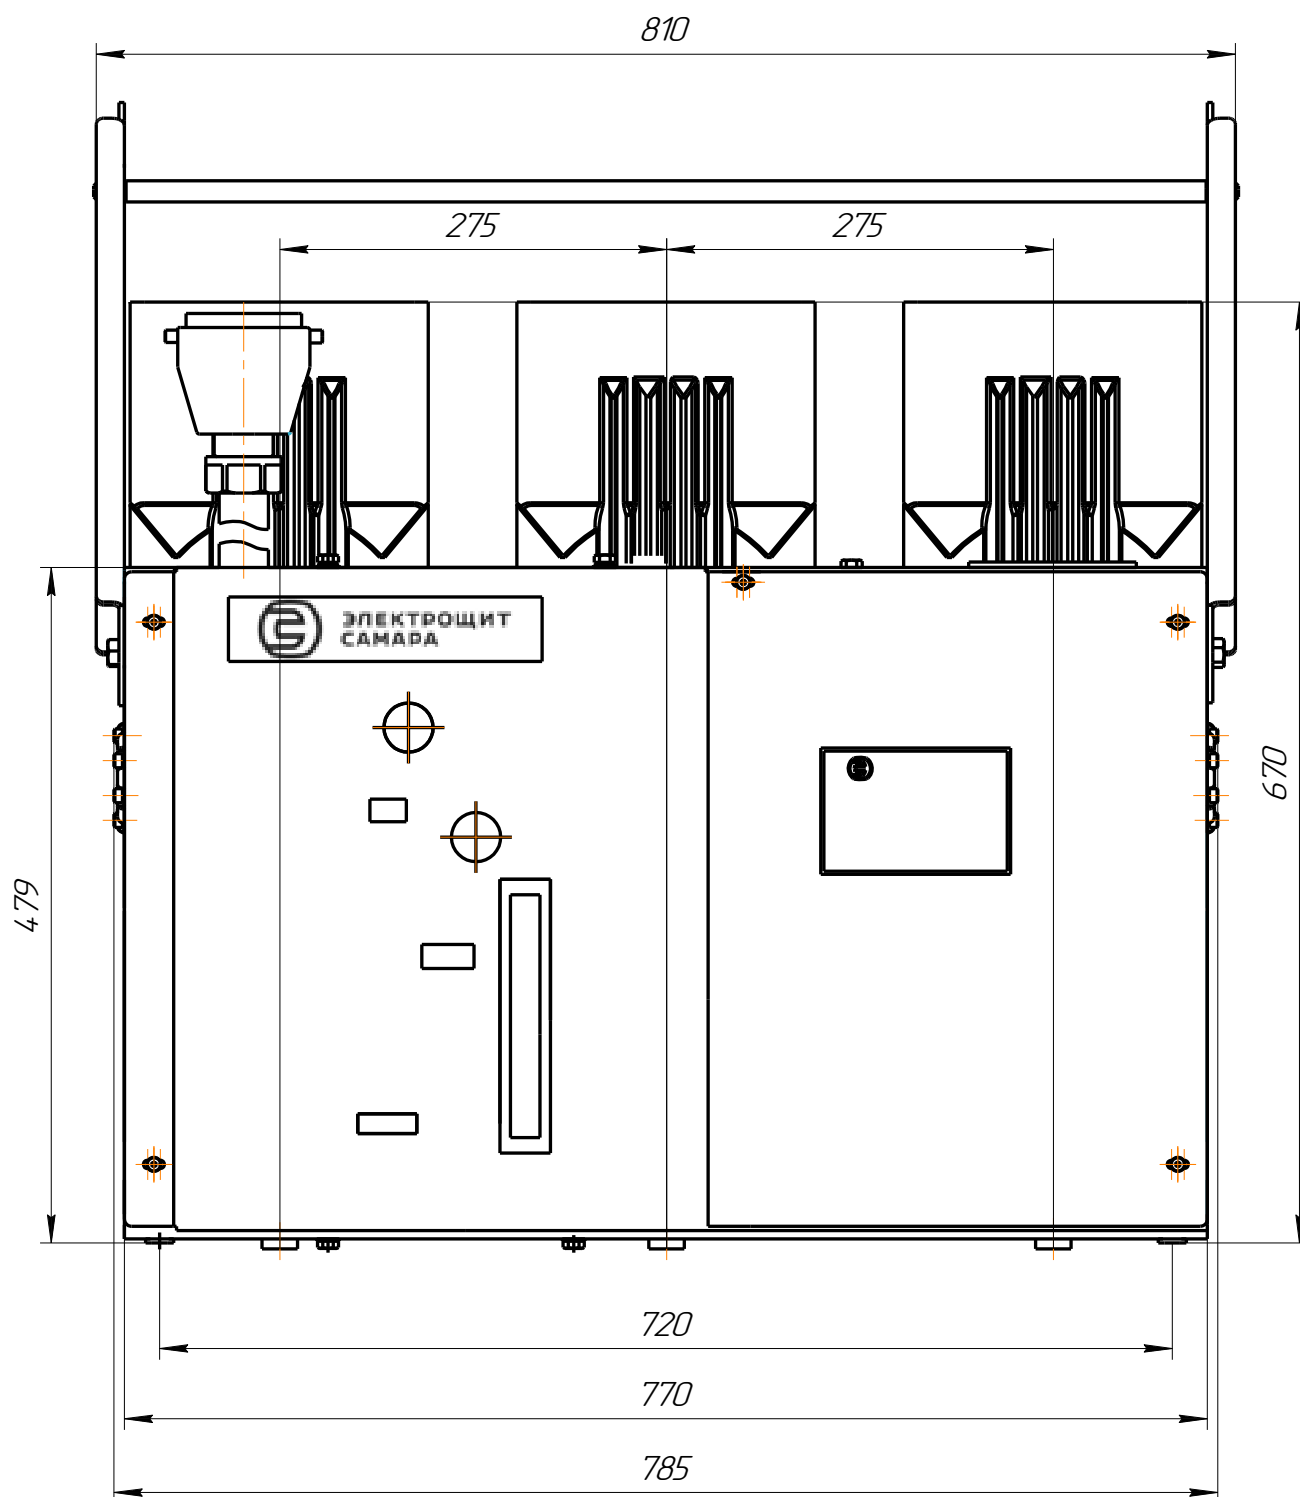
Габаритные и присоединительные размеры выключателя ВБУ-СЭЩ-10-50
